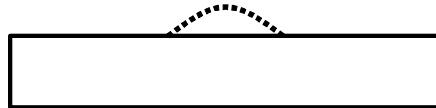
Зняття опуклості зварного шва механічною обробкою
